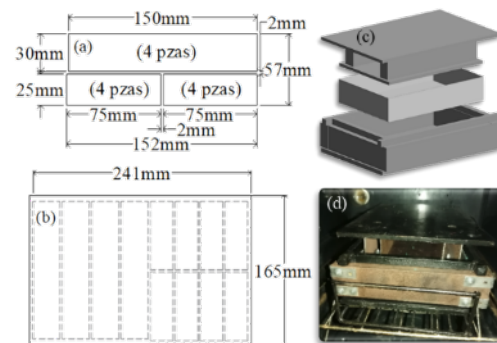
Proceso donde: (a) medidas probetas, (b) medida final muestra, (c) diseño del molde y (d) molde fabricado.
